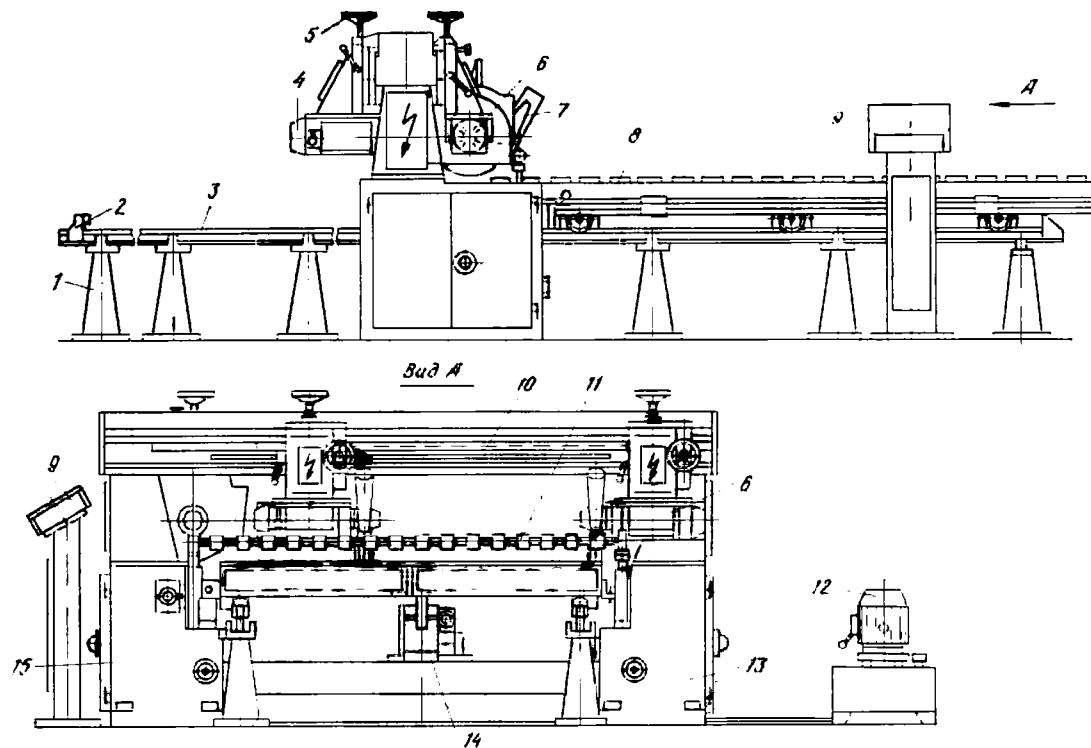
Схема форматно-обрезного станка ЦТЗФ-1:
